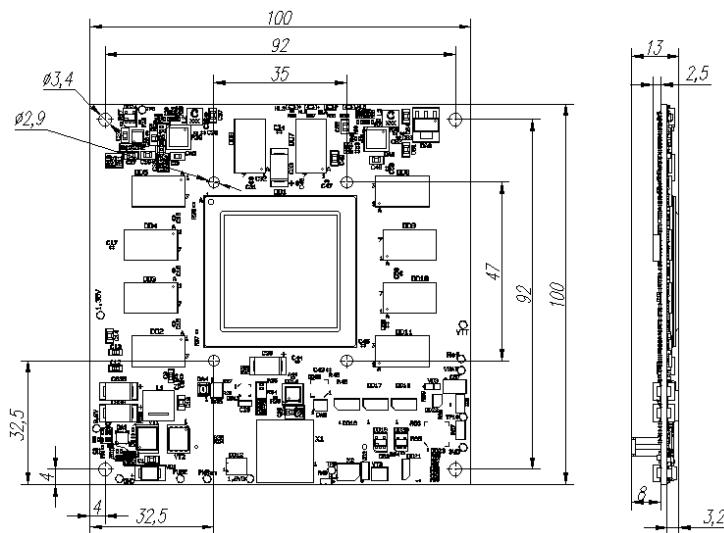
Габаритные и присоединительные размеры Модуля
